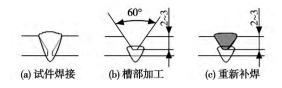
补焊试验过程示意图(mm) Fig. 1 Repair welding process
